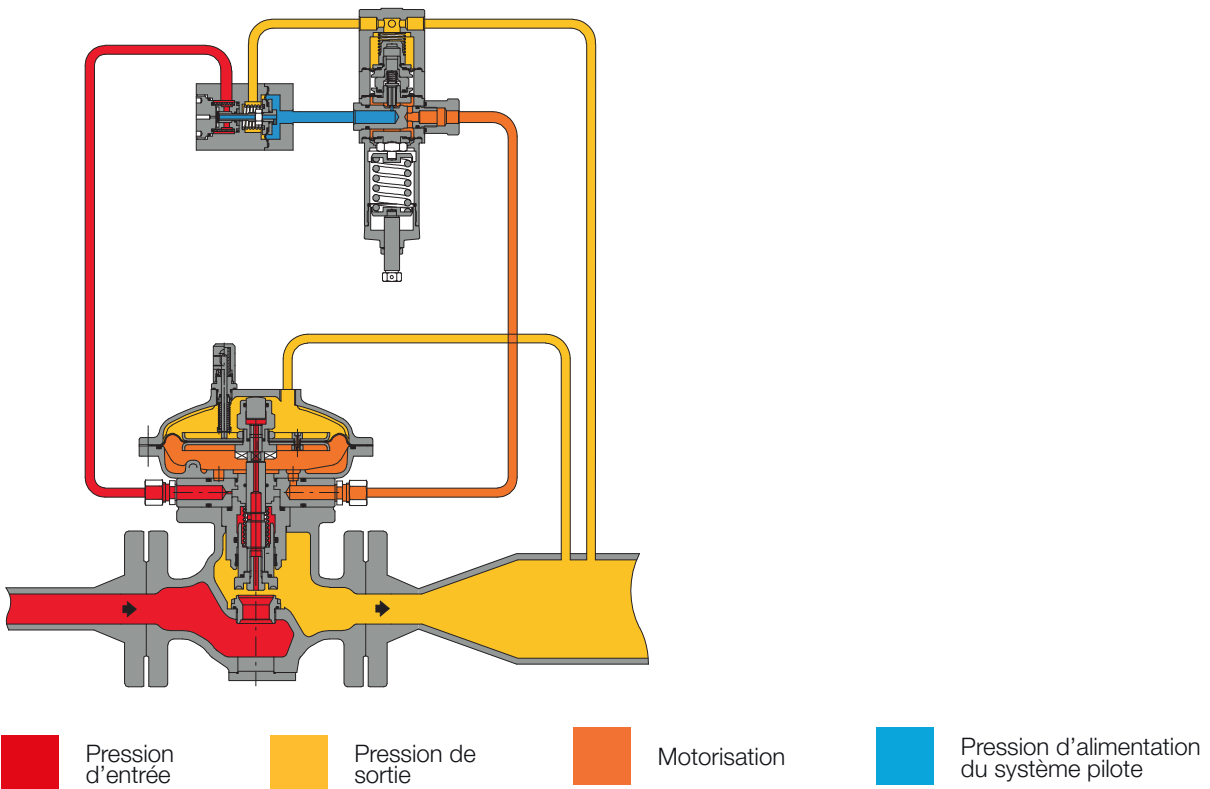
Dixi avec la série de pilotes 210 Fail Open.
